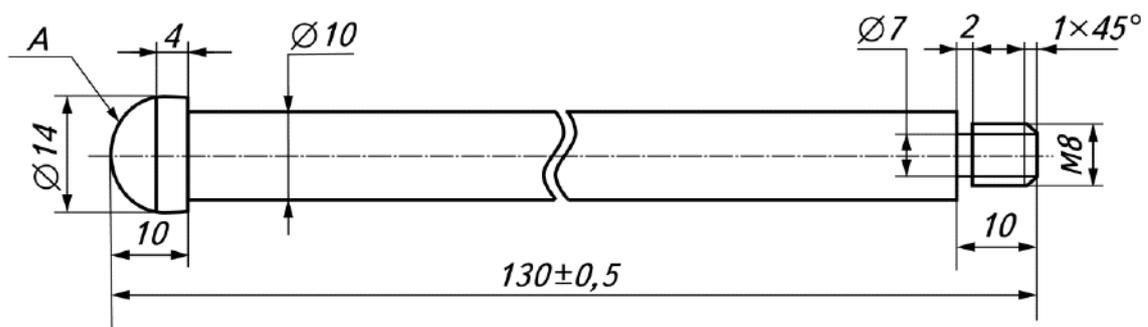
Рукоятка для винтового зажима столярного верстака
